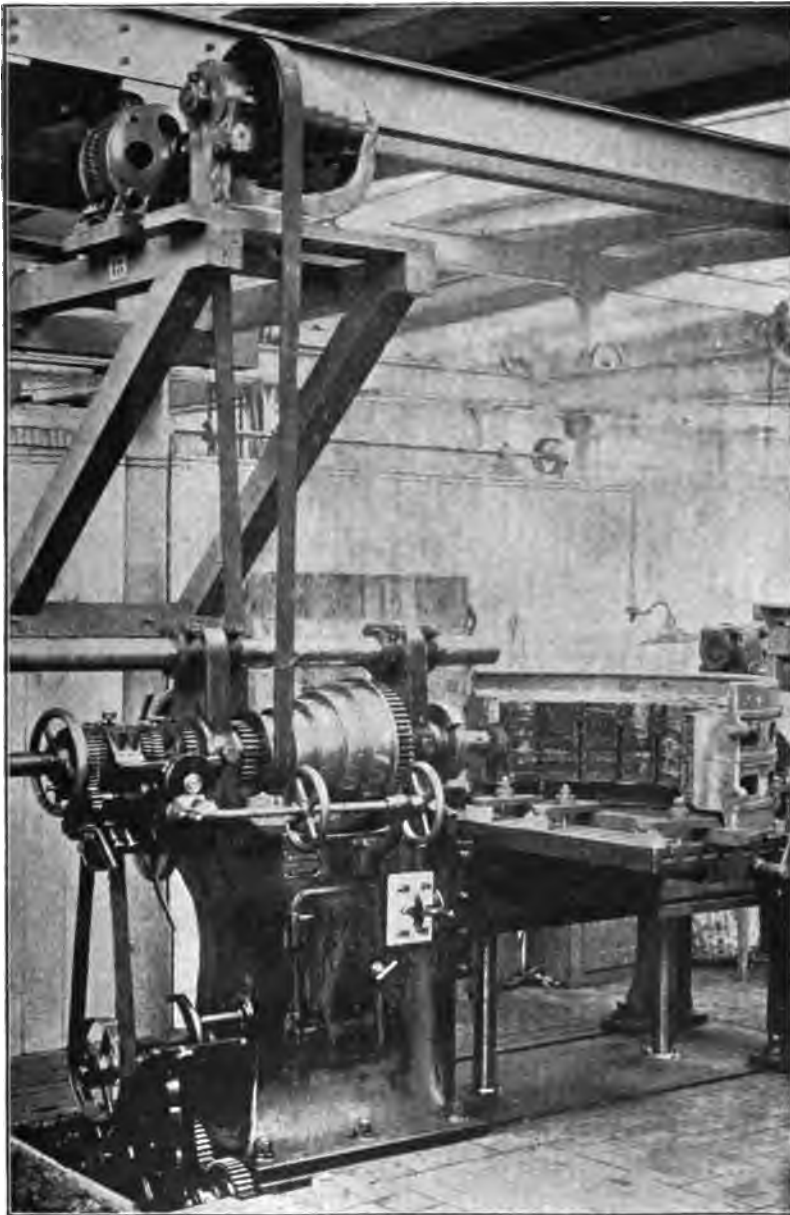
Drehbank oder Werkzeugmaschine mit Elektromotor
